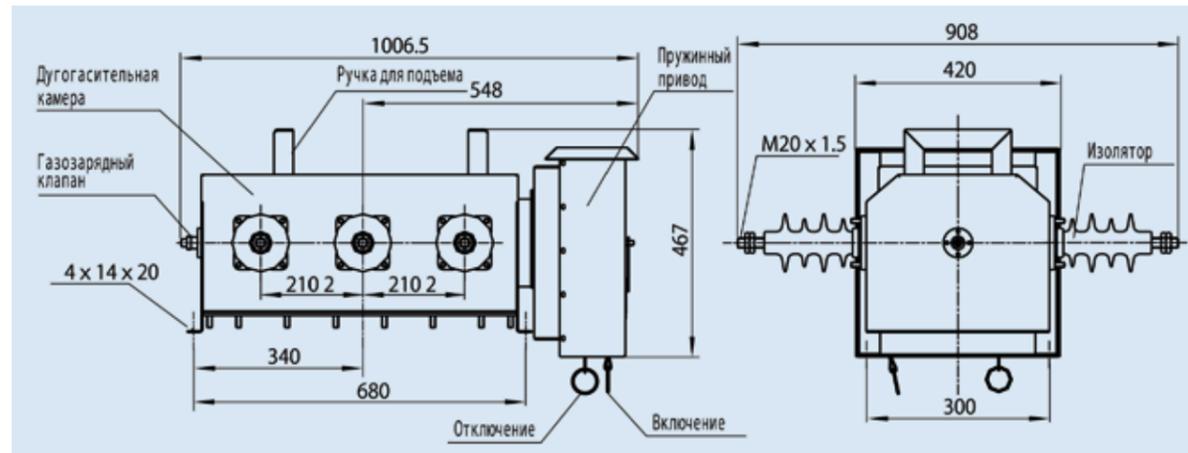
Внешний вид и размеры выключателя LW3-12
